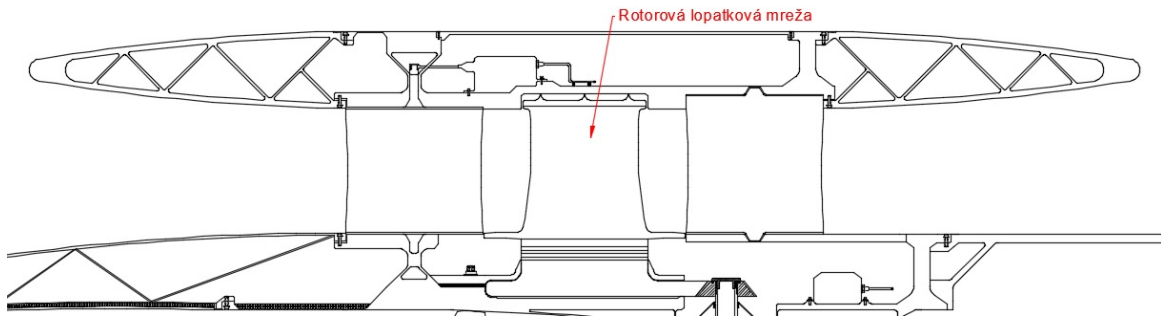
Uloženie rotorovej časti náporovej turbíny
